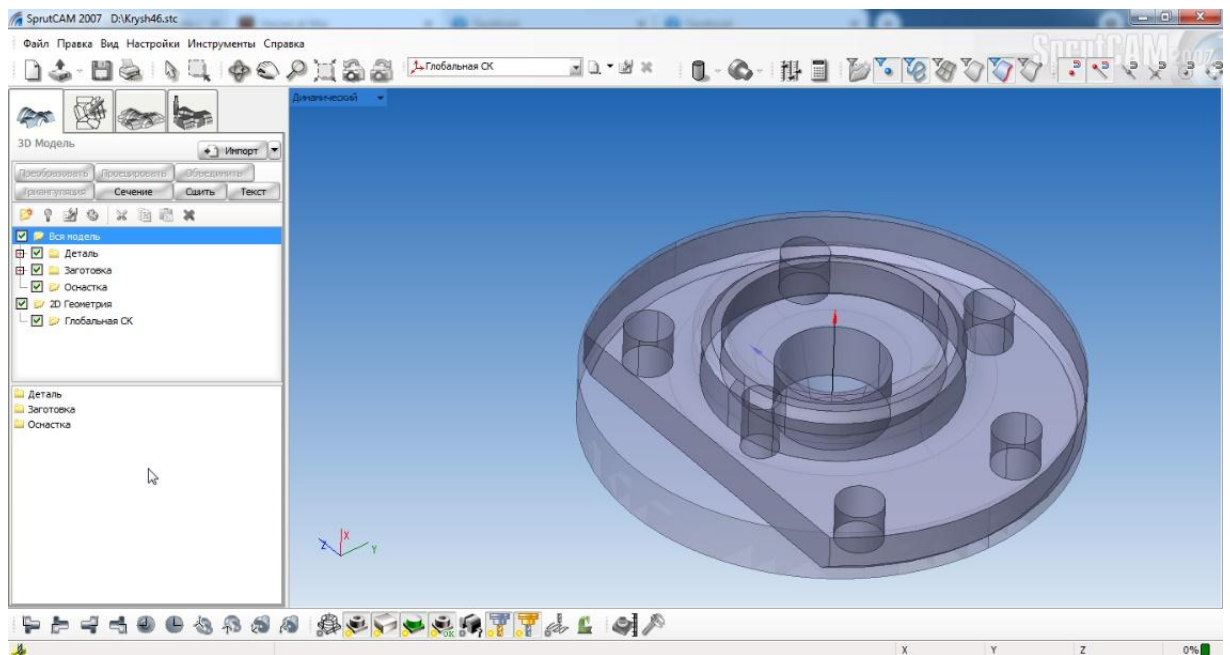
Деталь та заготовка, імпортовані в систему
